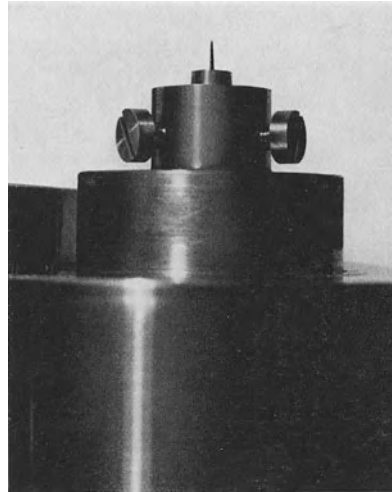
Seitenansicht des in die Vorrichtung eingesetzten Stahlzylinders mit Nadel.
